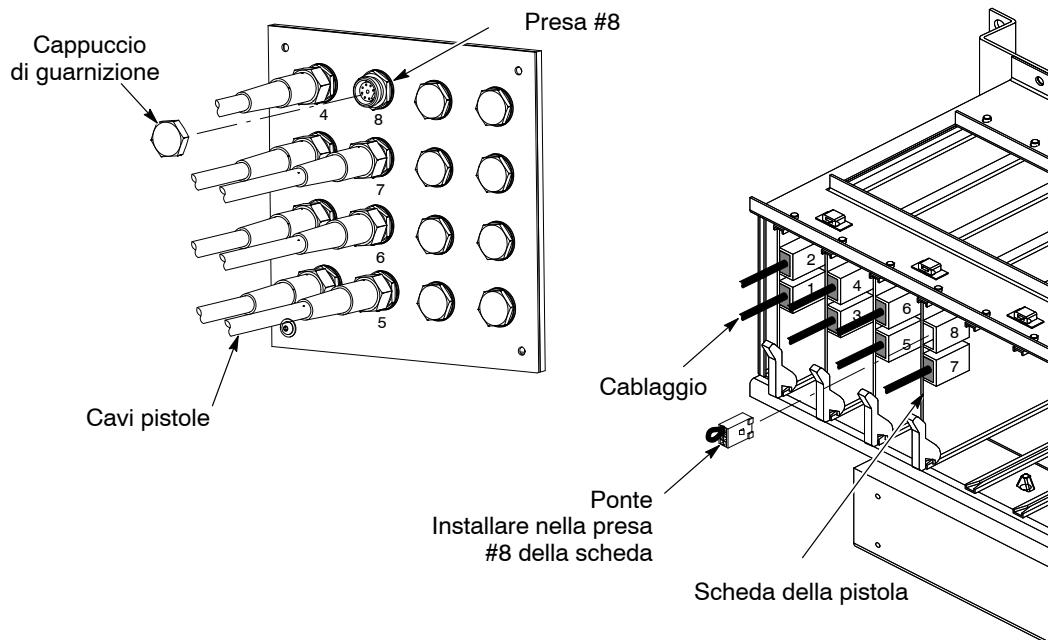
Installazione di guarnizione e ponte – Esempio di sistema da 8 pistole con 7 pistole
